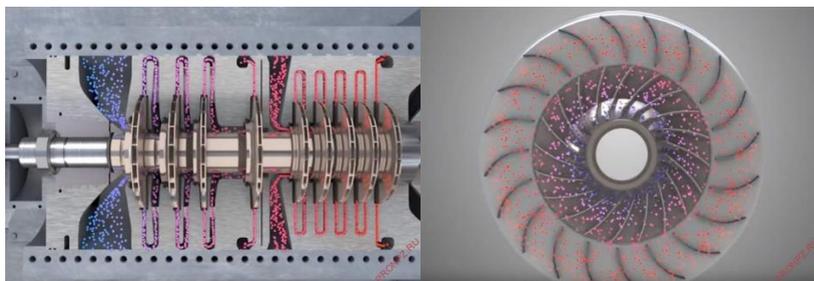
Центробежный компрессор      Рис. 2. Ротор компрессора
